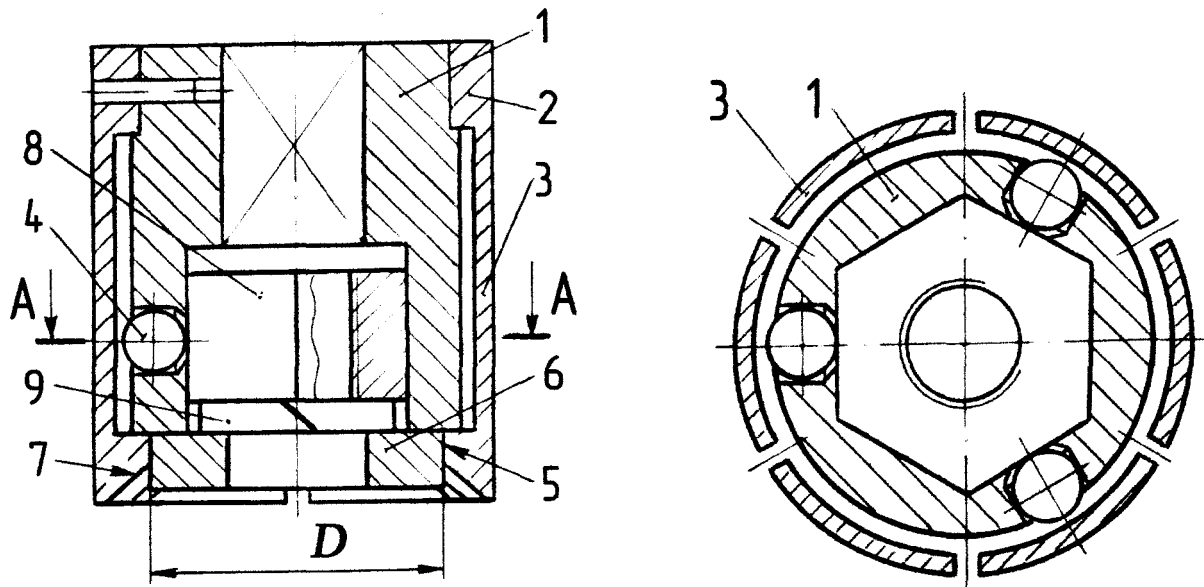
Головка для захоплення гайок у комплекті з шайбами або без них: 1– торцева головка; 2– цанга; 3 – пелюстки цанги; 4 – кульки; 5– отвір під плоску шайбу 6 діаметром  $D$ ; 7– західна фаска; 8 – захоплена гайка; 9 – пружинна шайба.
